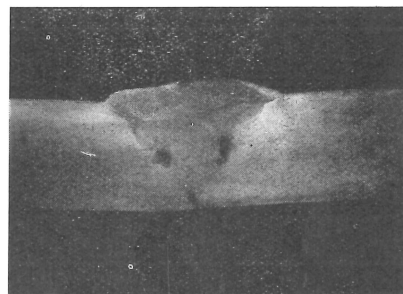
Coupe transversale dans la soudure représentée figure 13a.
